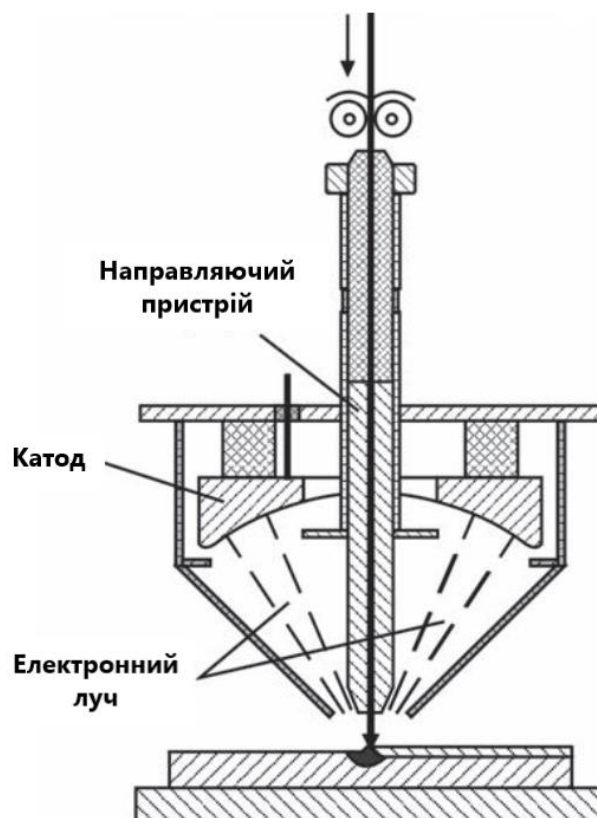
Схема пристрою для реалізації технології xBeam 3D Metal Printing [3]
